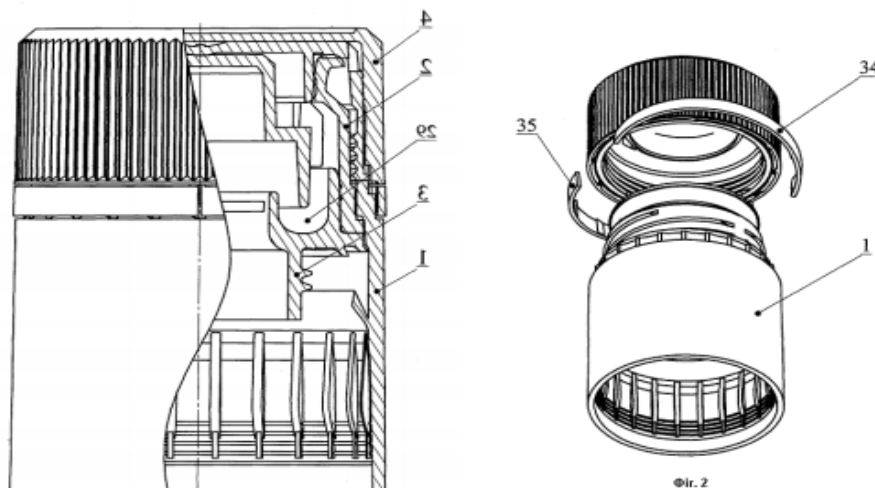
Схема закупорювального пристрою пляшки
